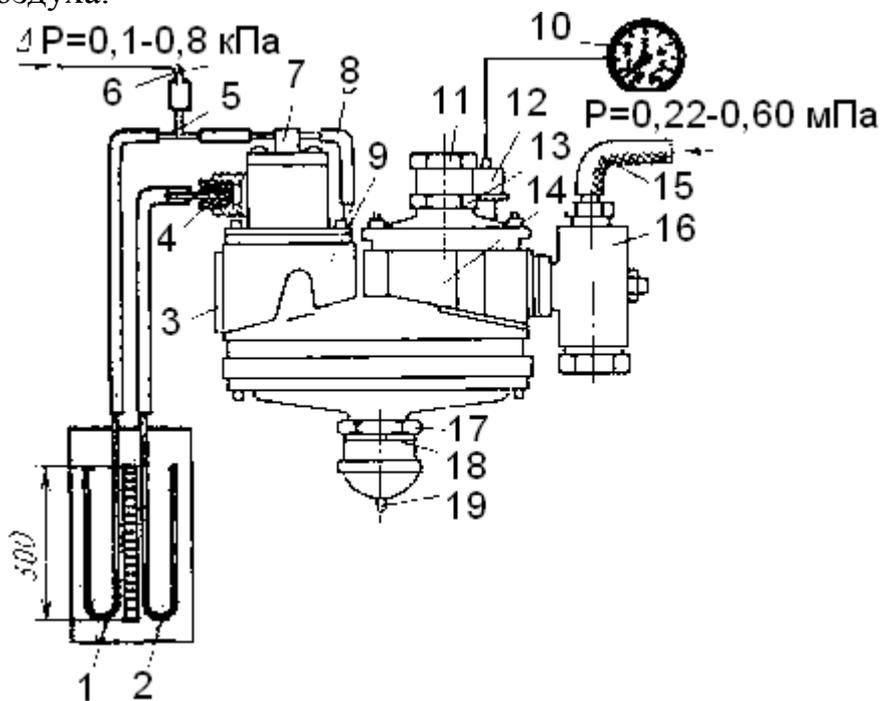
Регулировка редуктора низкого давления: 1,2-пьезометры, 3- крышка редуктора, 4-трубчатая пробка, 5-тройник, 6, 8, 15-трубки, 7-крышка экономайзерной установки, 9-вторая ступень редуктора, 10-манометр в кабине водителя, 11-регулирующая гайка первой ступени, 12- датчик манометра, 13,17-контргайка, 18-регулирующий ниппель второй ступени, 19- стержень штока
